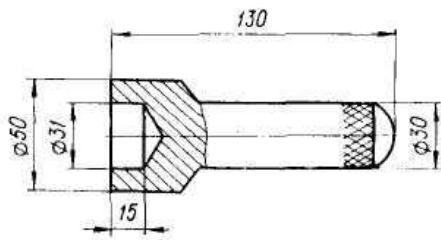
Оправка для напрессовки подшипника на зубчатый хвостовик
